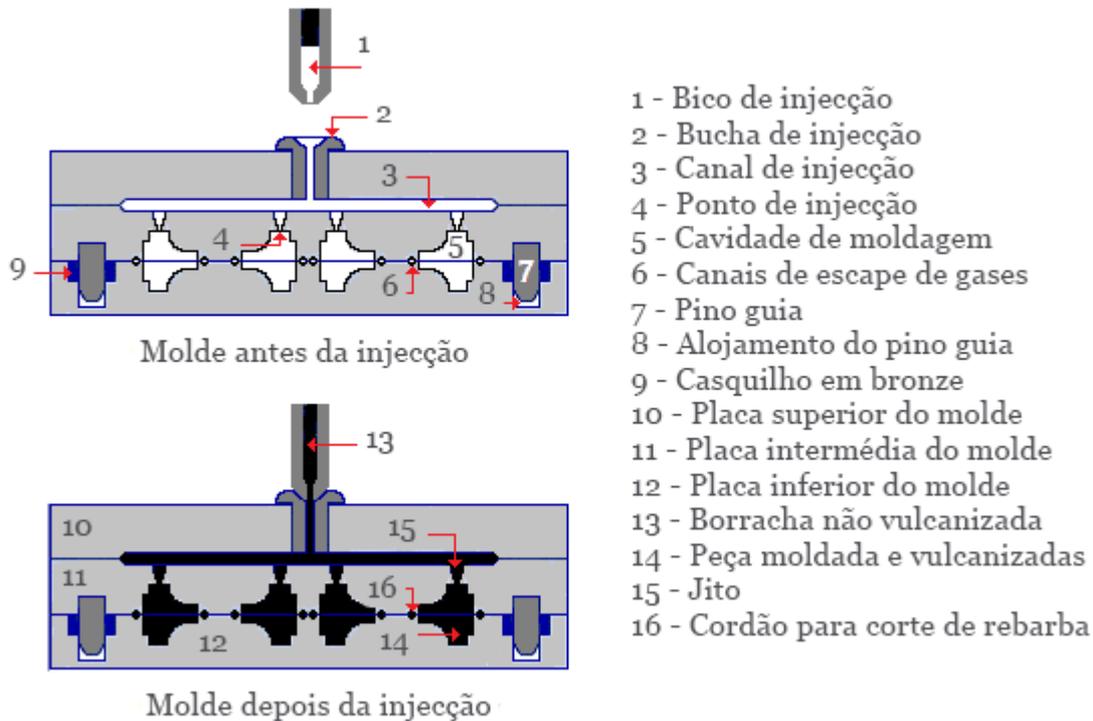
Molde para processo de moldagem por injeção (Caetano 2019).
